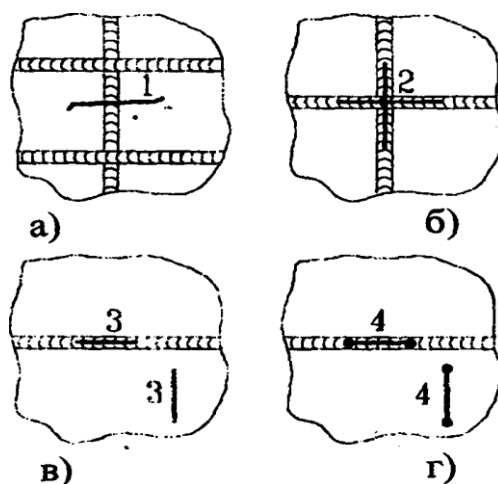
Трещины сварных соединений и основного металла стенки резервуара
